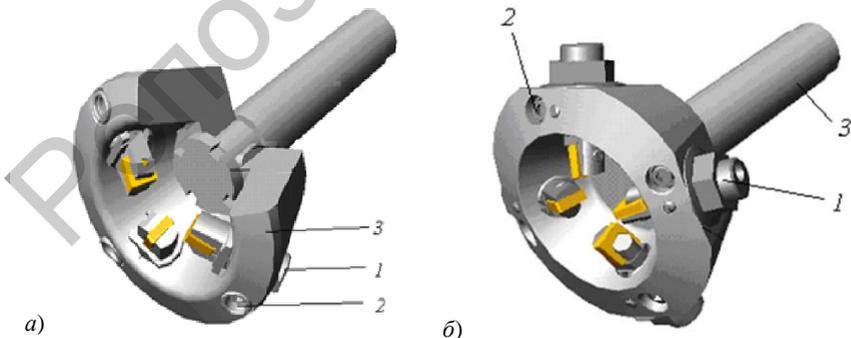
Конструкции сборных режущих инструментов для скоростной обработки сферических поверхностей без регулировки (а) и с микрометрической регулировкой (б) лезвий
